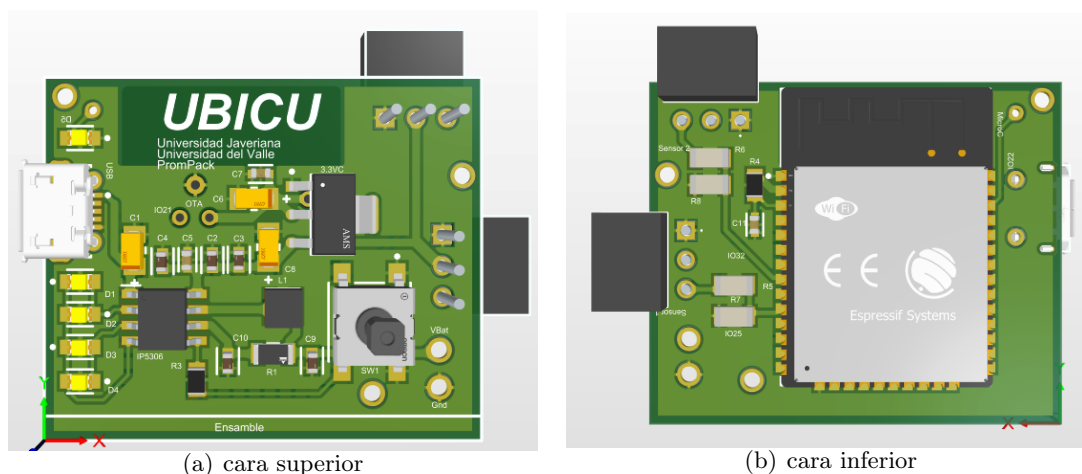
CAD PCB principal del segundo prototipo del dispositivo Ubicu.
